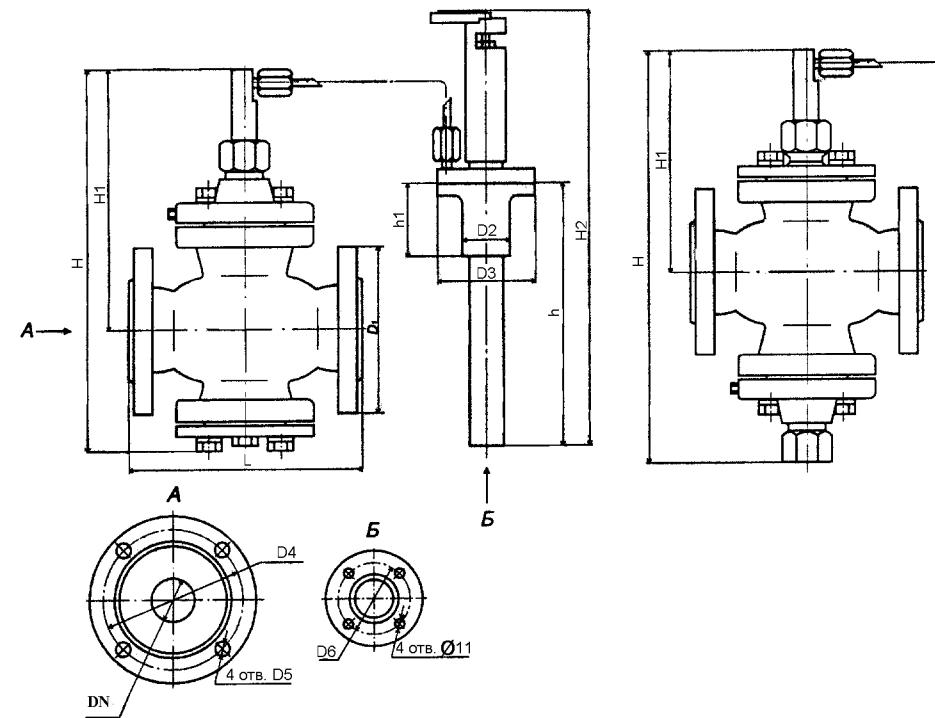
Габаритные и присоединительные размеры регуляторов РТ.
